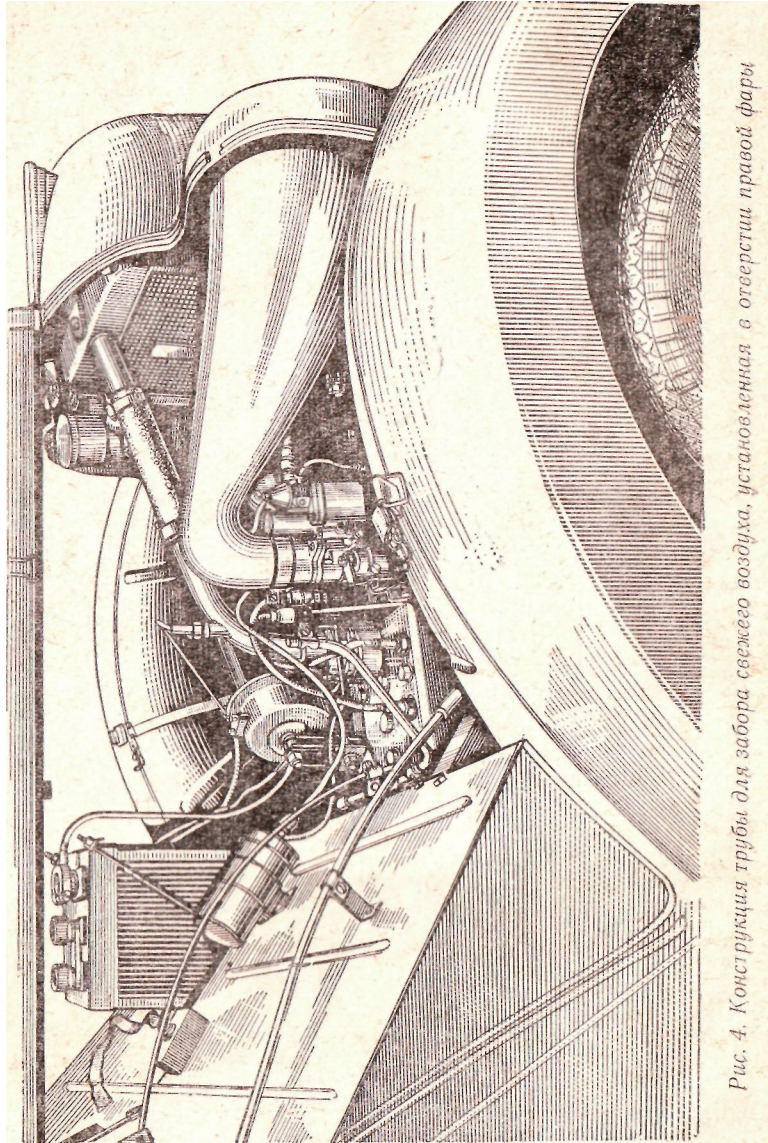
Конструкция трубы для забора свежего воздуха, установленная в отверстии правой фары
